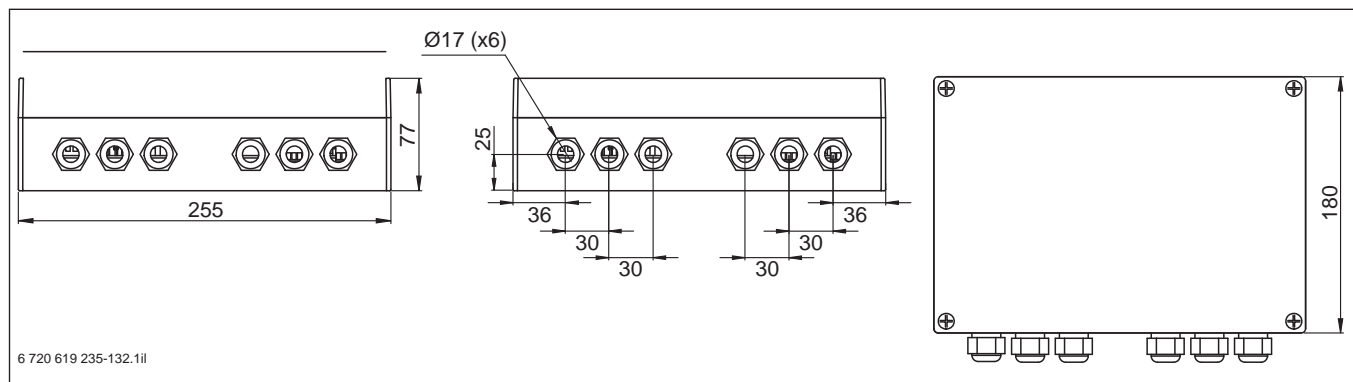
Abmessungen Multimodul HHM17-1 (Maße in mm)
